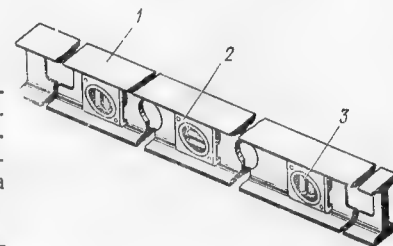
1 — корпус; 2 — крышка; 3 — ампулы
